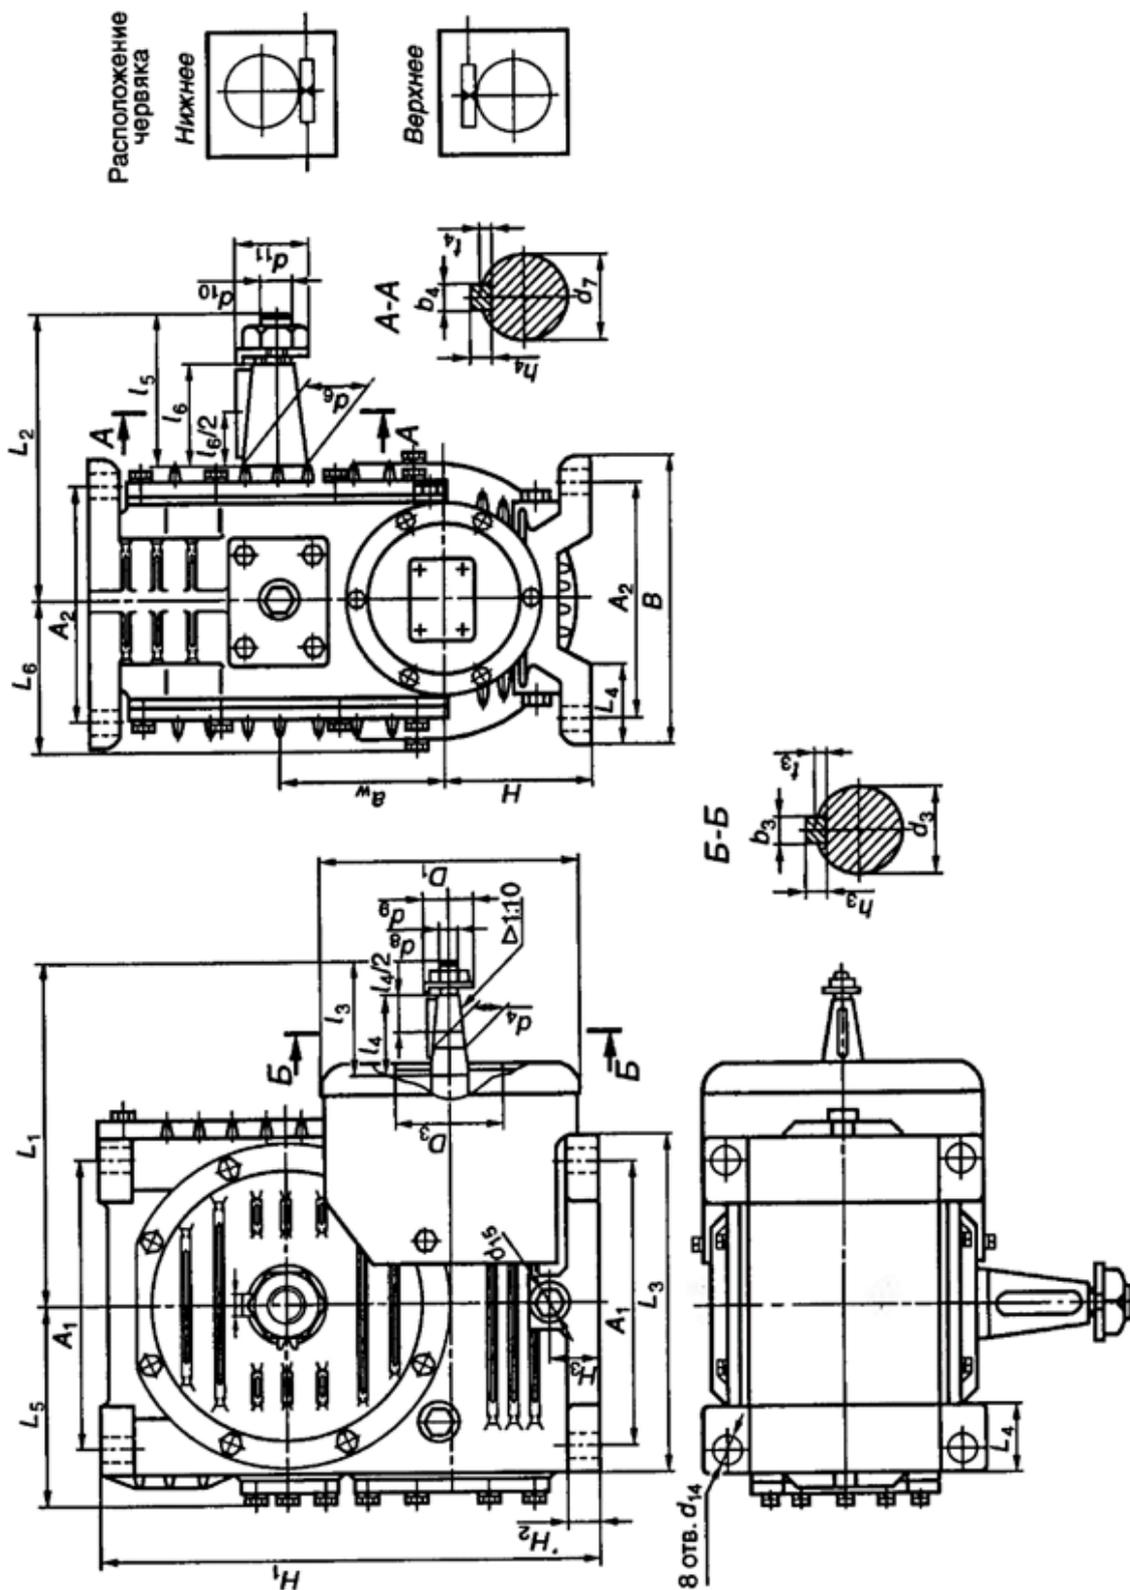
Габаритные и присоединительные размеры червячных редукторов Ч-100, Ч-125, Ч-160
